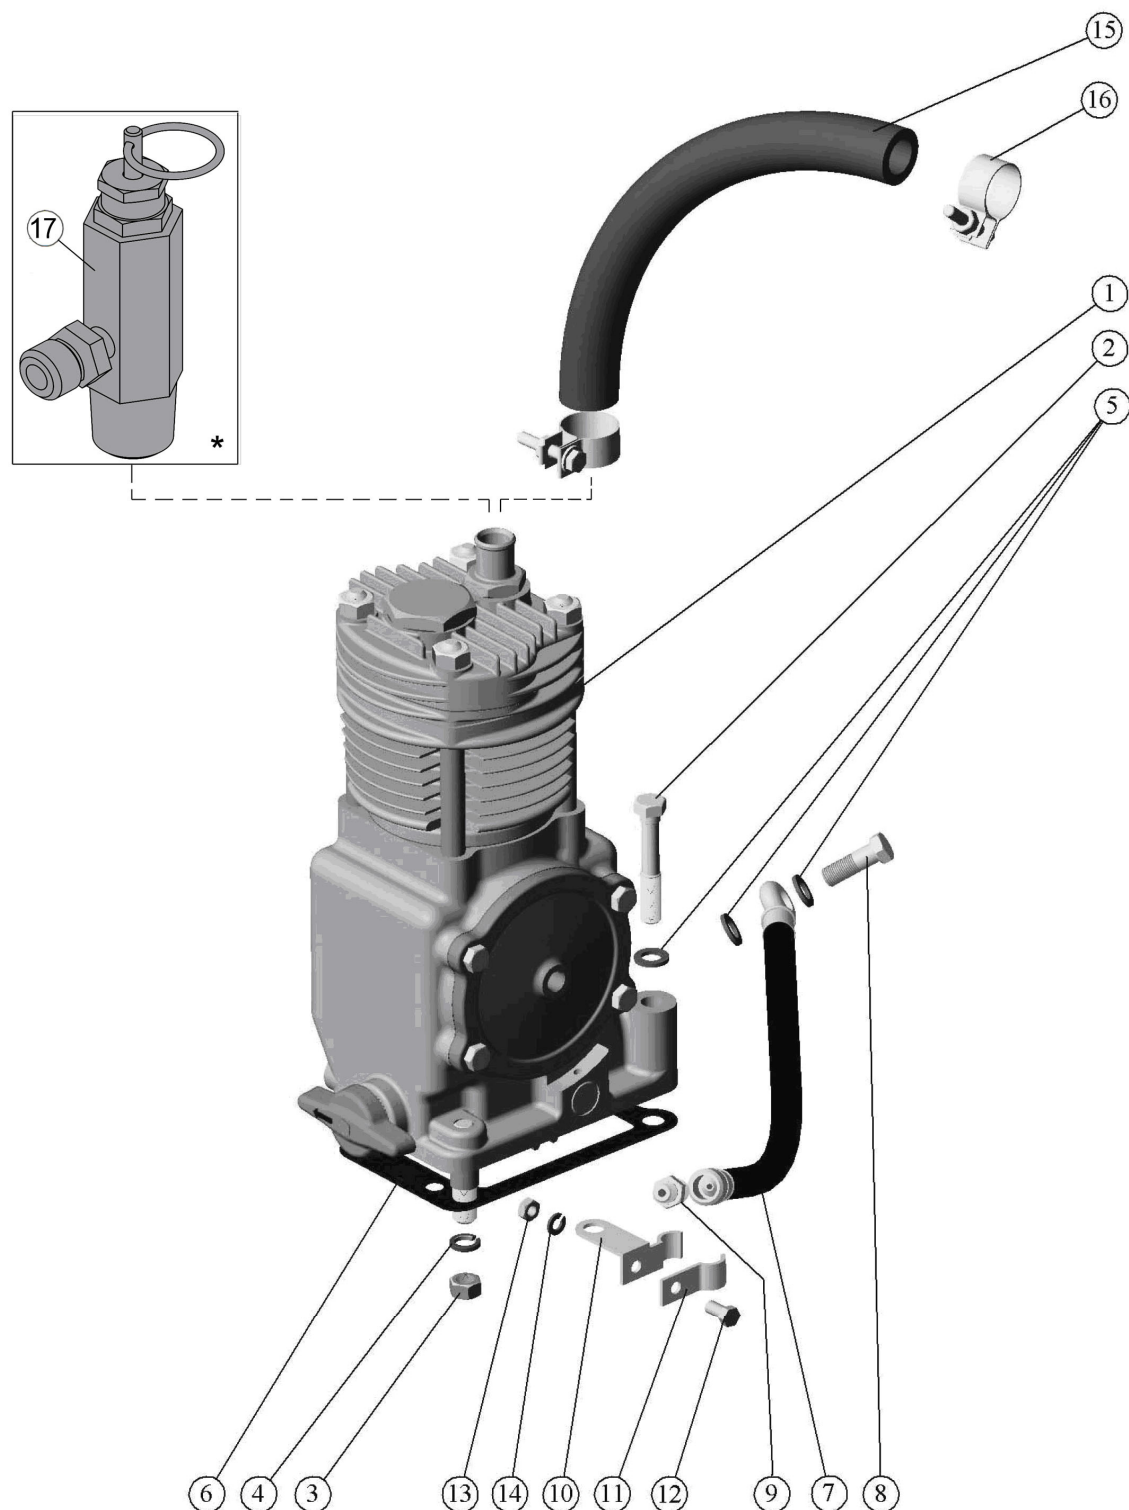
Установка пневмокомпрессора (для двигателей Д-242)
